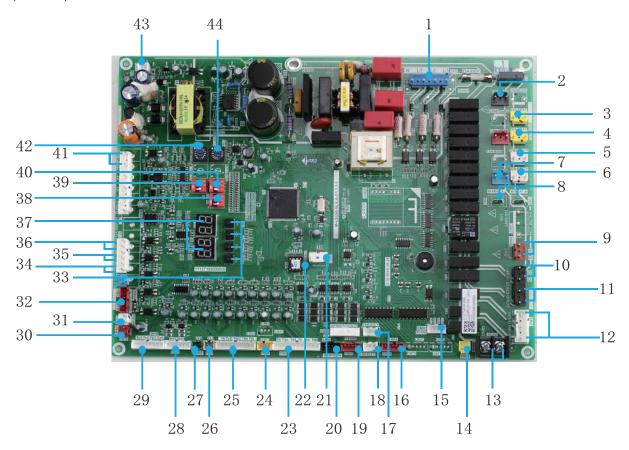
PCB principal de las unidades HTW-MCSU30MRN8LR32 y HTW-MCSU60MRN8LR32
